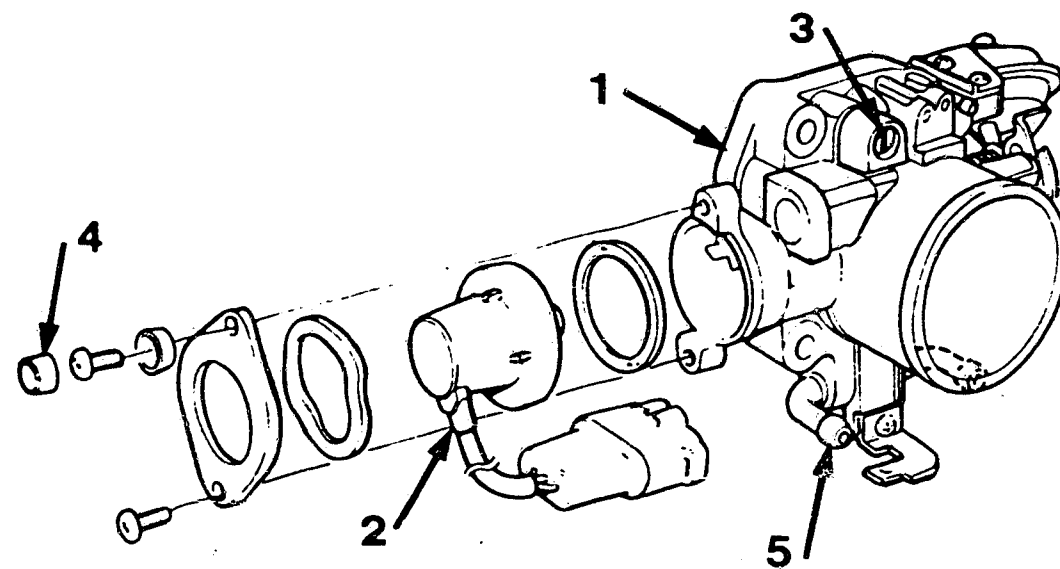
Drosselklappengehäuse (1) mit Drosselklappen-Winkelsensor (2) und Leerlauf Einstellschraube (3). Die Befestigungsschrauben sind mit einer Plastikkappe (4) gesichert. 5 Unterdruckanschluss.
